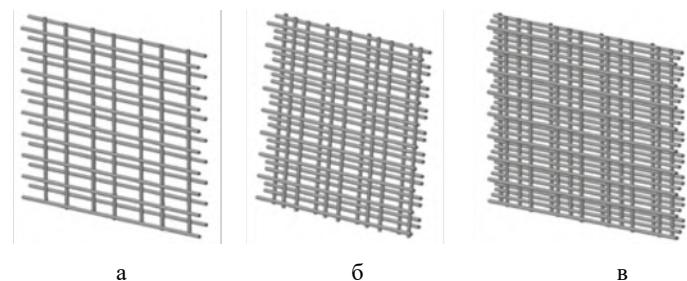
Сетка-заготовка для изготовления пулерассеивающих противоосколочных панелей сварных
